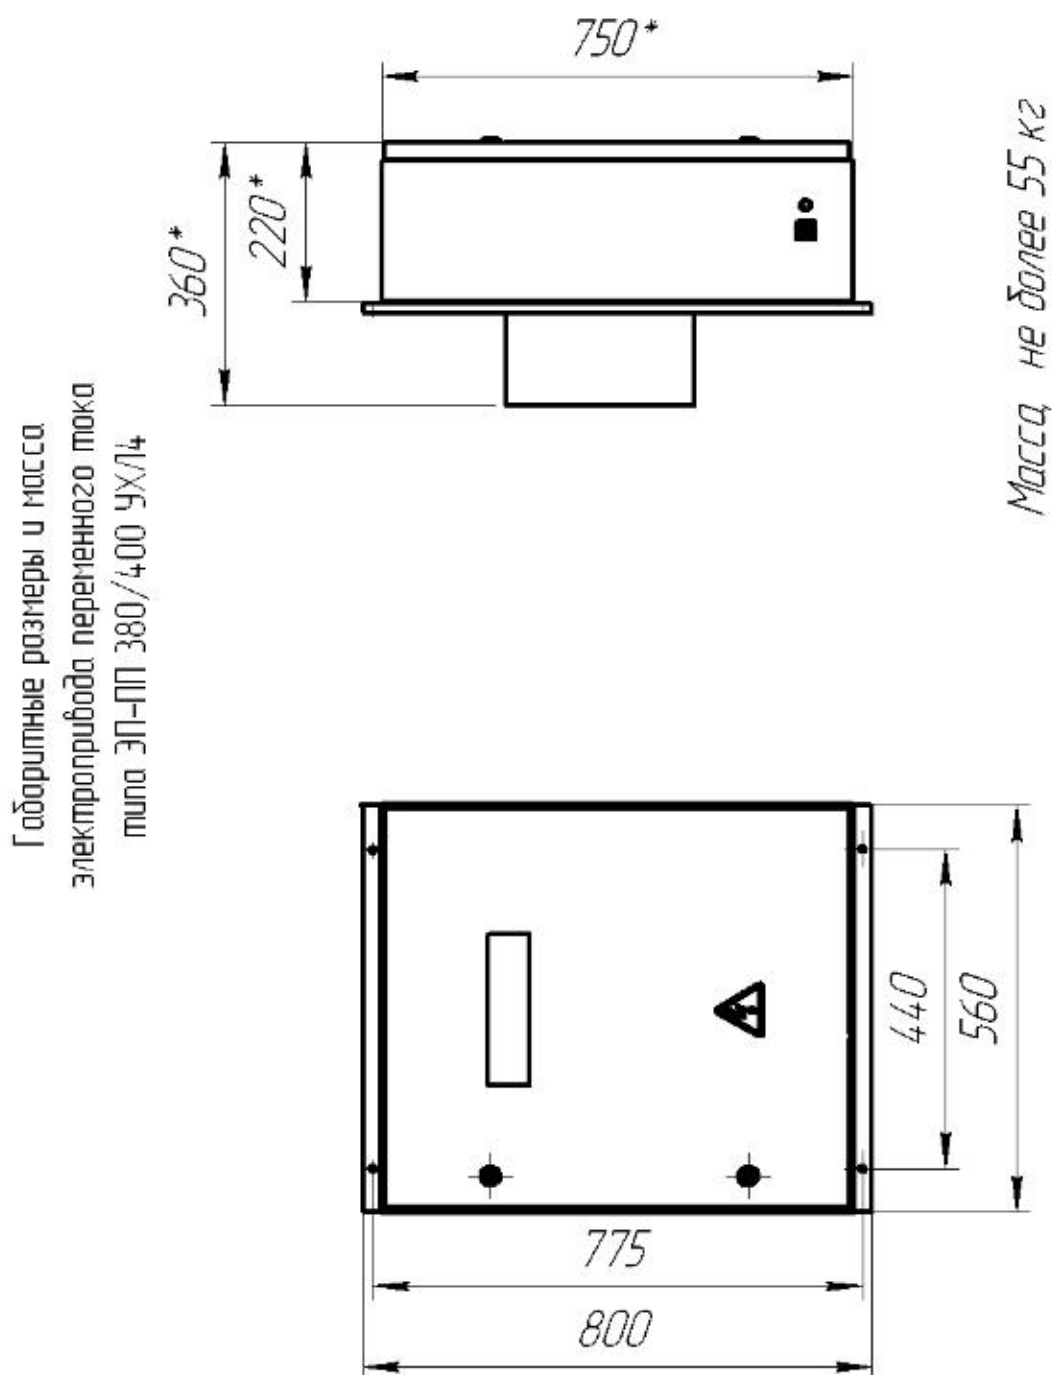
г Габаритные и установочные размеры ЭП-ПП-11 380/400
